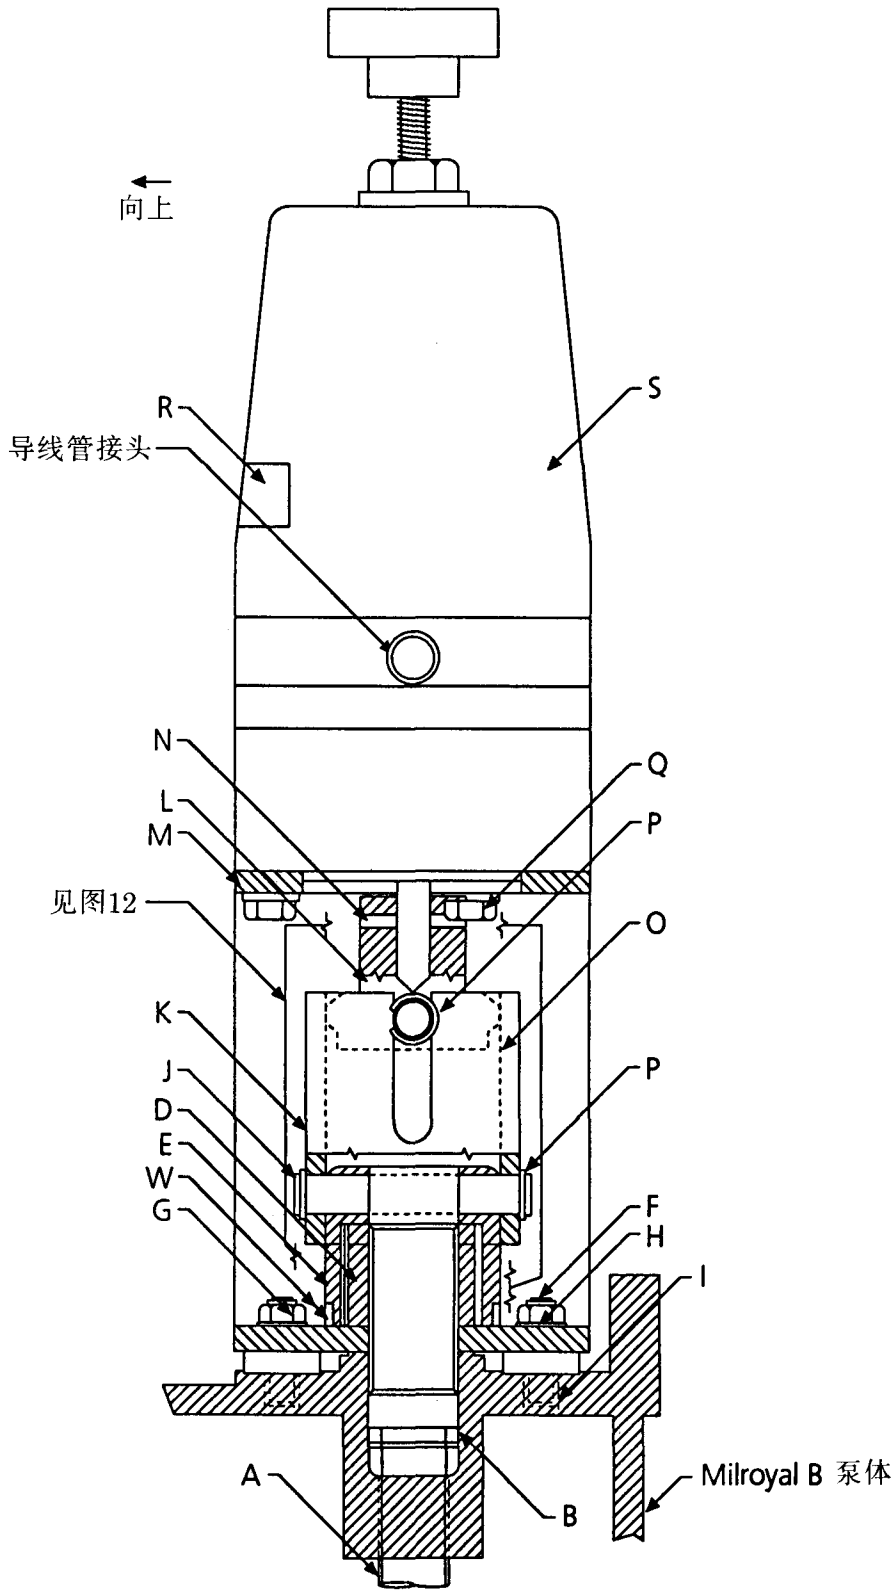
Milroyal B安装匹配器零件图(D-102-1507-000)
